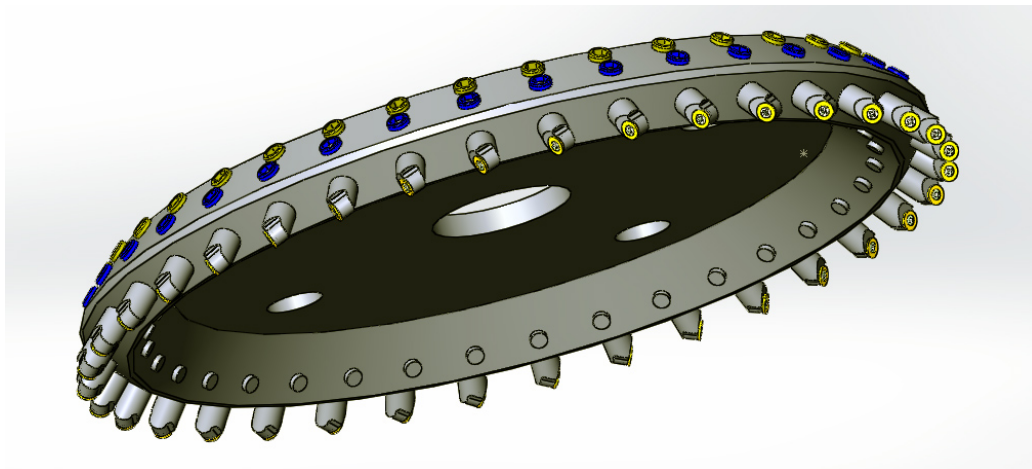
Торцева фреза з циліндричними різальними вставками та додатковими стопорними гвинтами
